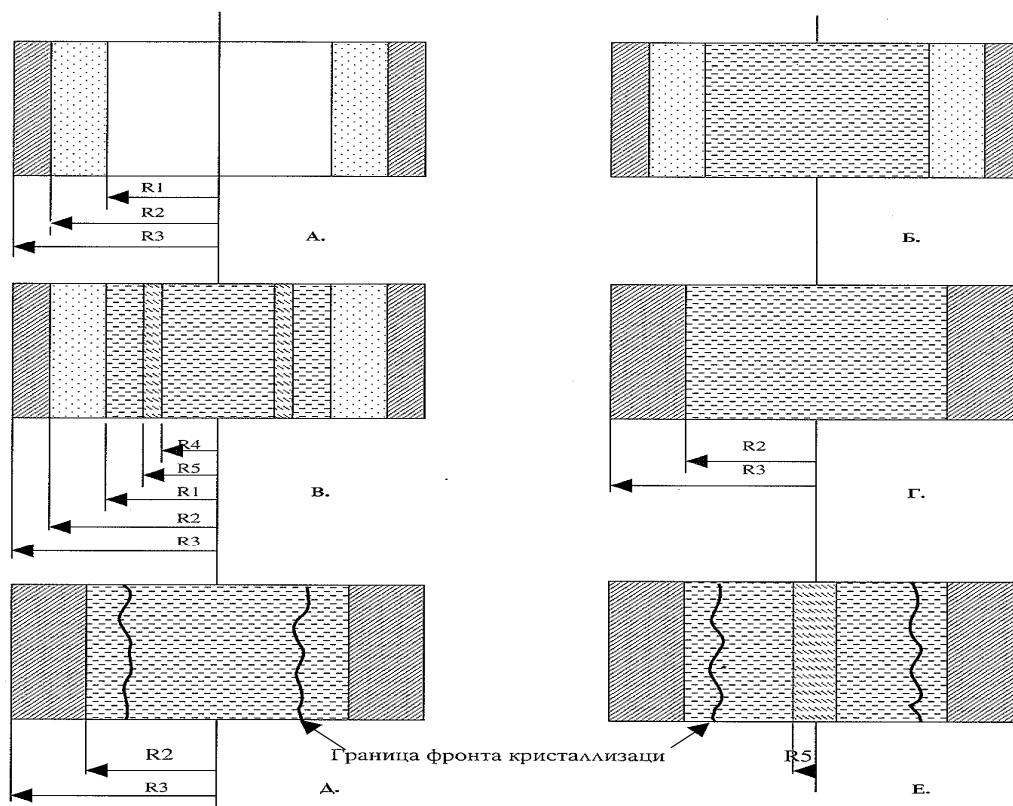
Схема формы для литья вала на различных этапах моделирования: А - Исходные размеры шейки прокатного вала; Б - Этап заполнения формы в шейках отливки; В - Вариант погружения в расплав плавкого модификатора трубчатого сечения; Г - Этап заполнения формы в зоне бочки отливки; Д - Этап формирования рабочего слоя вала; Е - Момент ввода модификатора на штанге
